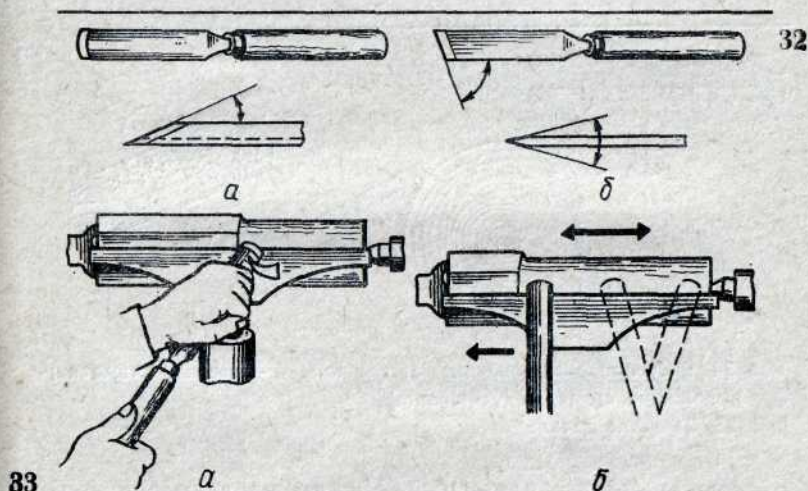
Резцы для работы на токарном станке: а — полукруглая стамеска; б — косая стамеска.
